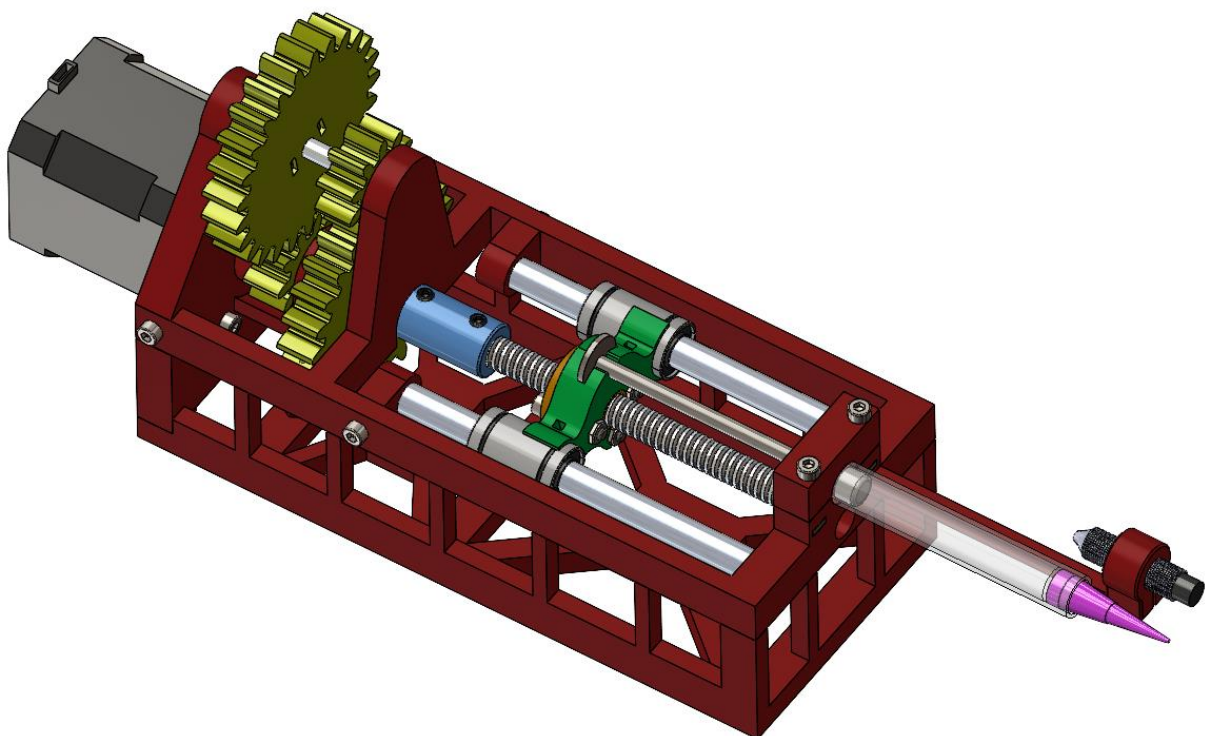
Ensamblaje del sistema extrusor de pastas.
